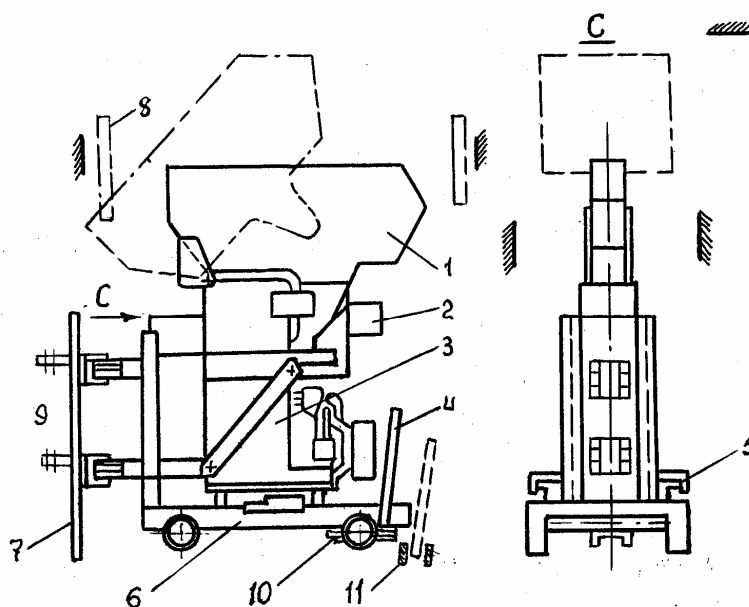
Конструкция выключателя ВАТ-42: 1 – дугогасительная камера; 2 – индукционно-динамический привод; 3 – полюс; 4 – рукоятка; 5 – пластина заземления; 6 – тележка; 7 – панель; 8 – изоляционный экран; 9 – контактная система цепей управления; 10 – защёлка; 11 – упор
